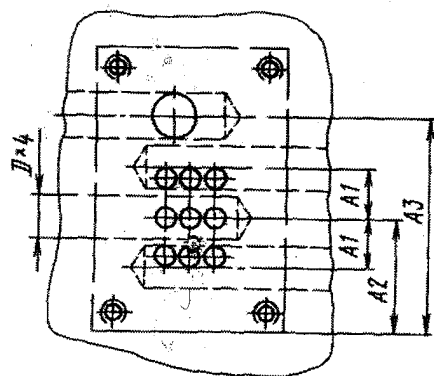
Габаритные и присоединительные размеры пневмораспределителей резьбового исполнения B64-23A-03, B64-24A-03, B64-25A-03
